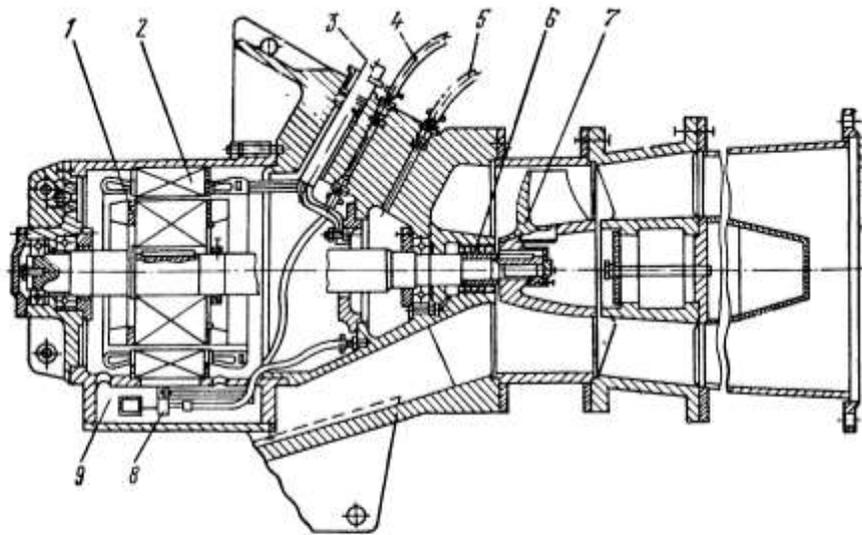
Конструкция погружного моноблочного осевого насоса типа ОПВ. 1 — ротор электродвигателя; 2 — статор; 3 — силовой кабель; 4 — сброс воды из двигателя; 5 — подача сжатого воздуха в двигатель; 6 — уплотнительный узел; 7 — рабочее колесо насоса; 8 — сигнализатор протечек воды; 9 — сборник
